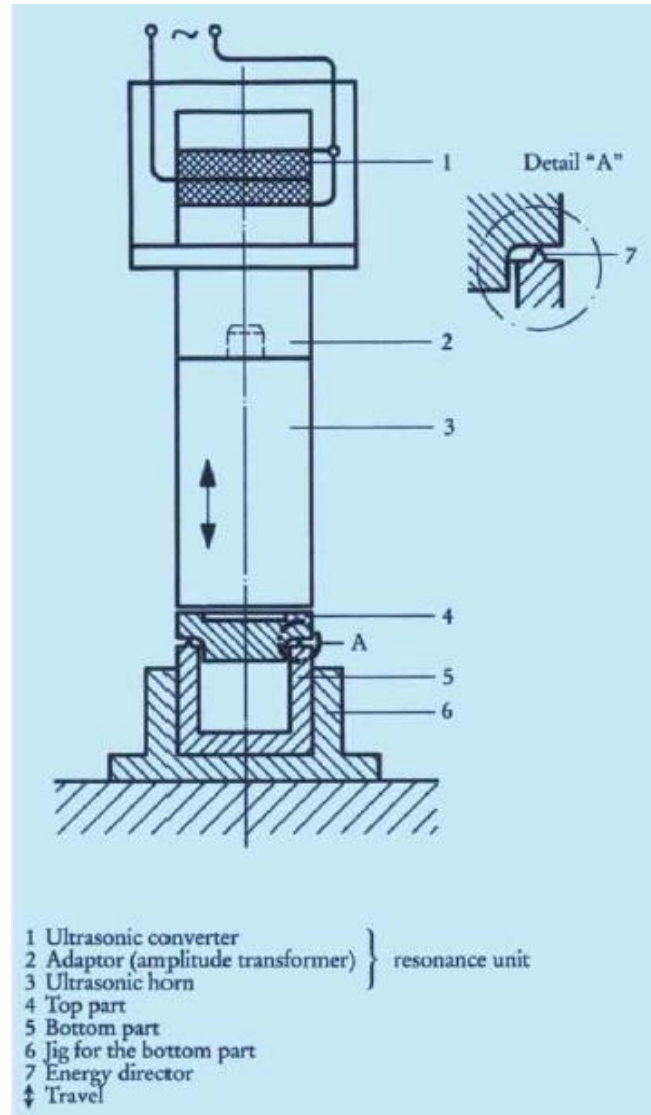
Esquema del funcionament d'una unitat de soldadura per ultrasons [10]
